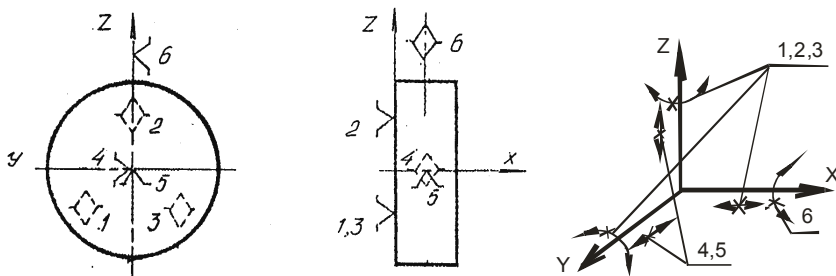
Теоретическая схема базирования заготовки типа диска по оси цилиндрической и плоской поверхностям
